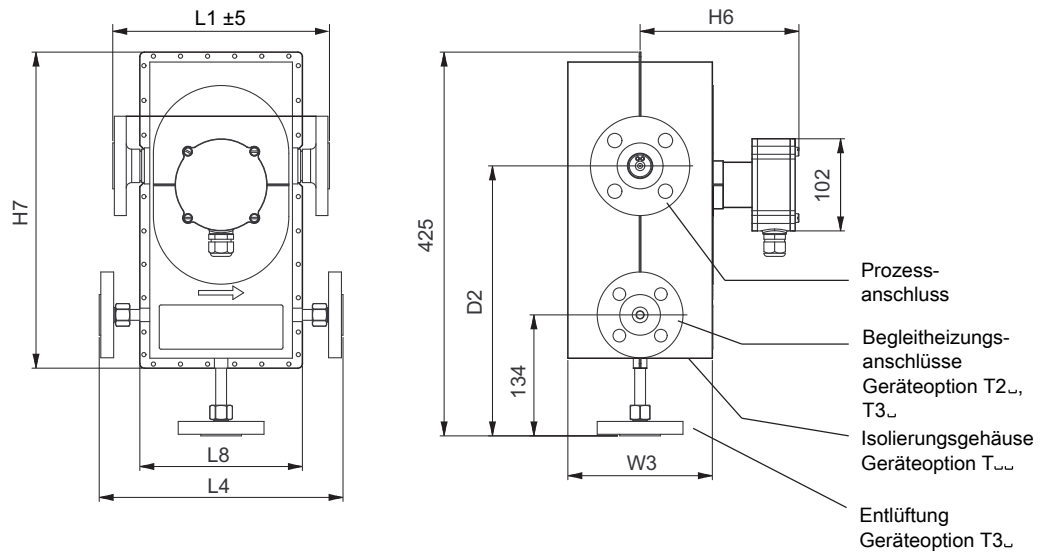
Abmessungen in mm: Variante mit Isolierungsgehäuse
